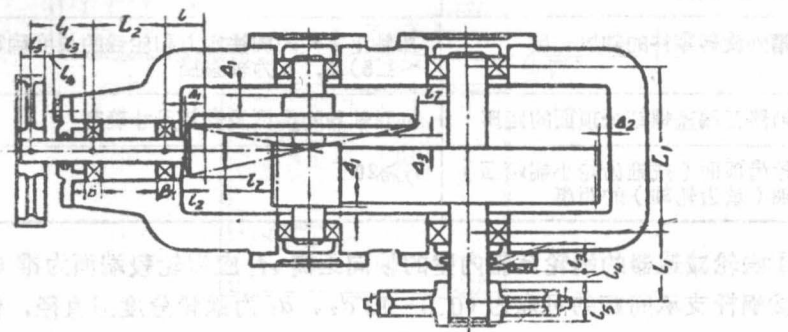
圆锥—圆柱齿轮减速器零件的位置尺寸
